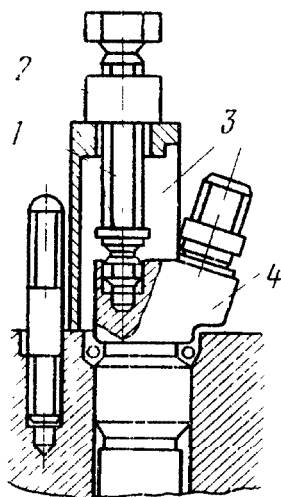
Снятие форсунки с двигателя съемником И-801.11.000:
